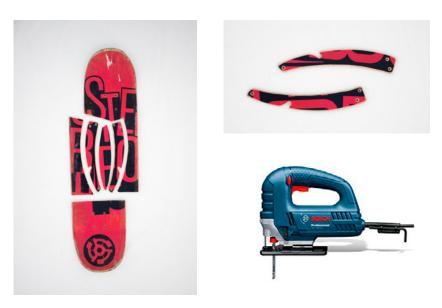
, 29. Posicion original en la tabla y geometría tras corte de los soportes. Figura 30. Sierra de calar.
